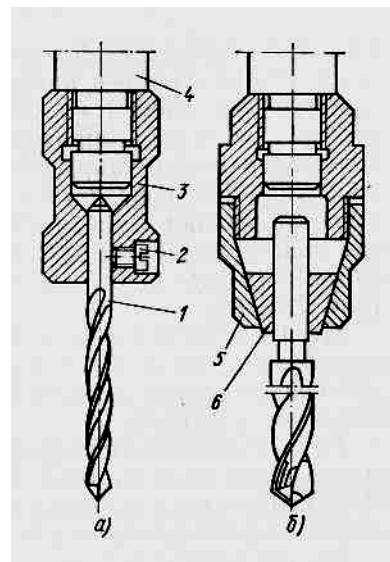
Установка сверлильного инструмента на шпинделе:
